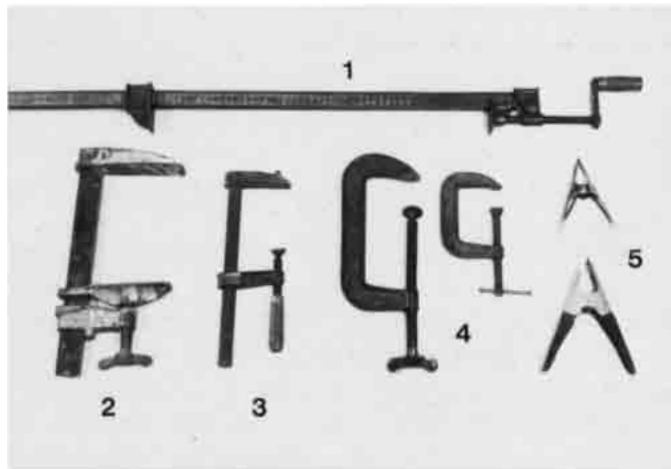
Schraubzwingen: (1) Schraubknecht; (2) Schraubzwinde, schwere Ausführung; (3) Schraubzwinde; (4) C-Schraubzwinde; (5) Feder-Zwingen.
